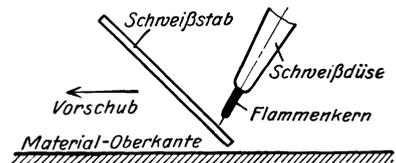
Führung des Brenners bei Messing- und Aluminiumschweißungen.
